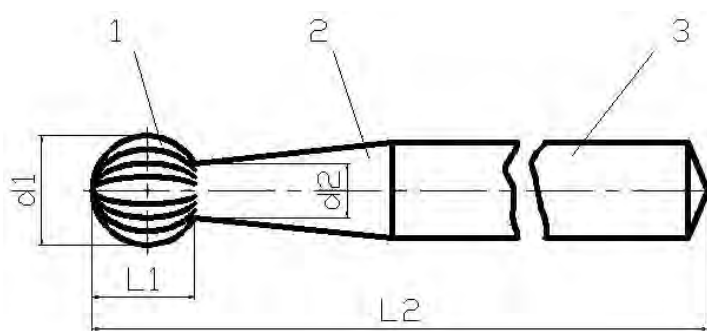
Конструкция зубного бора: d_1 – диаметр рабочей части (головки); d_2 – диаметр шейки; L_1 – длина рабочей части; L_2 – общая длина бора
